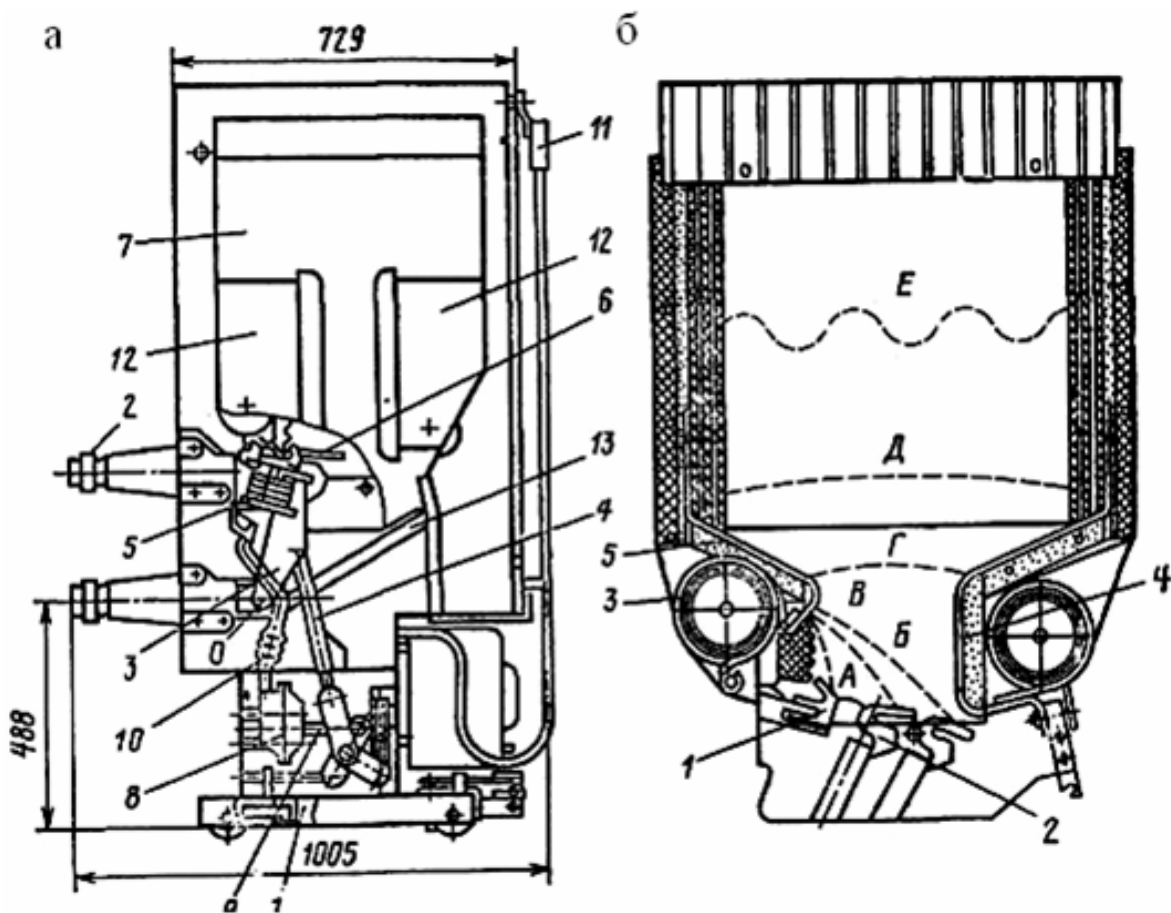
Электромагнитный выключатель: *а* - общий вид выключателя;
